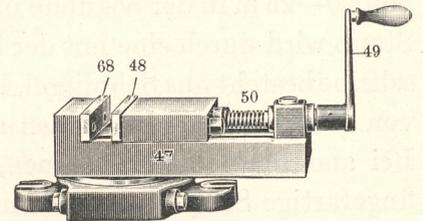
Drehbarer Schraubstock der Universalfräsmaschine.
